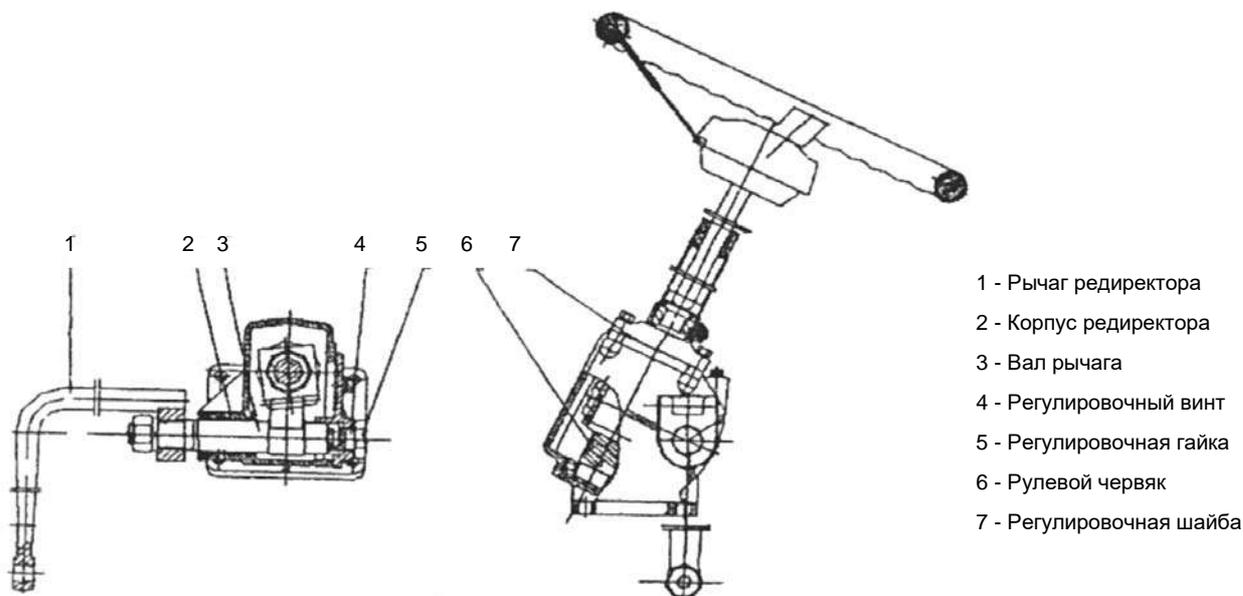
Редилятор с шаром, зубчатой рейкой и зубчатым сектором
